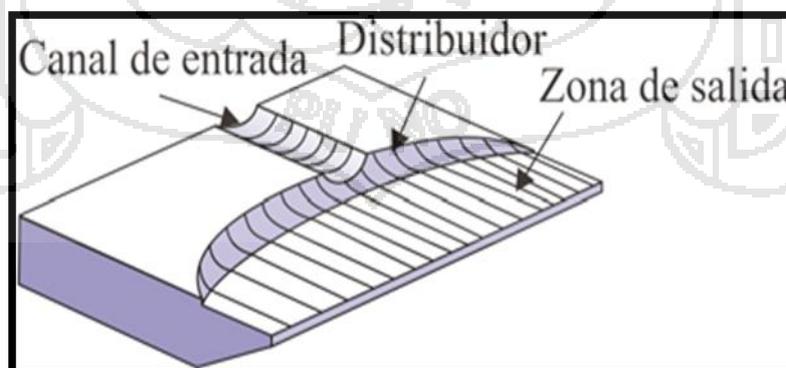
Partes diferenciadas en una boquilla de extrusión.
